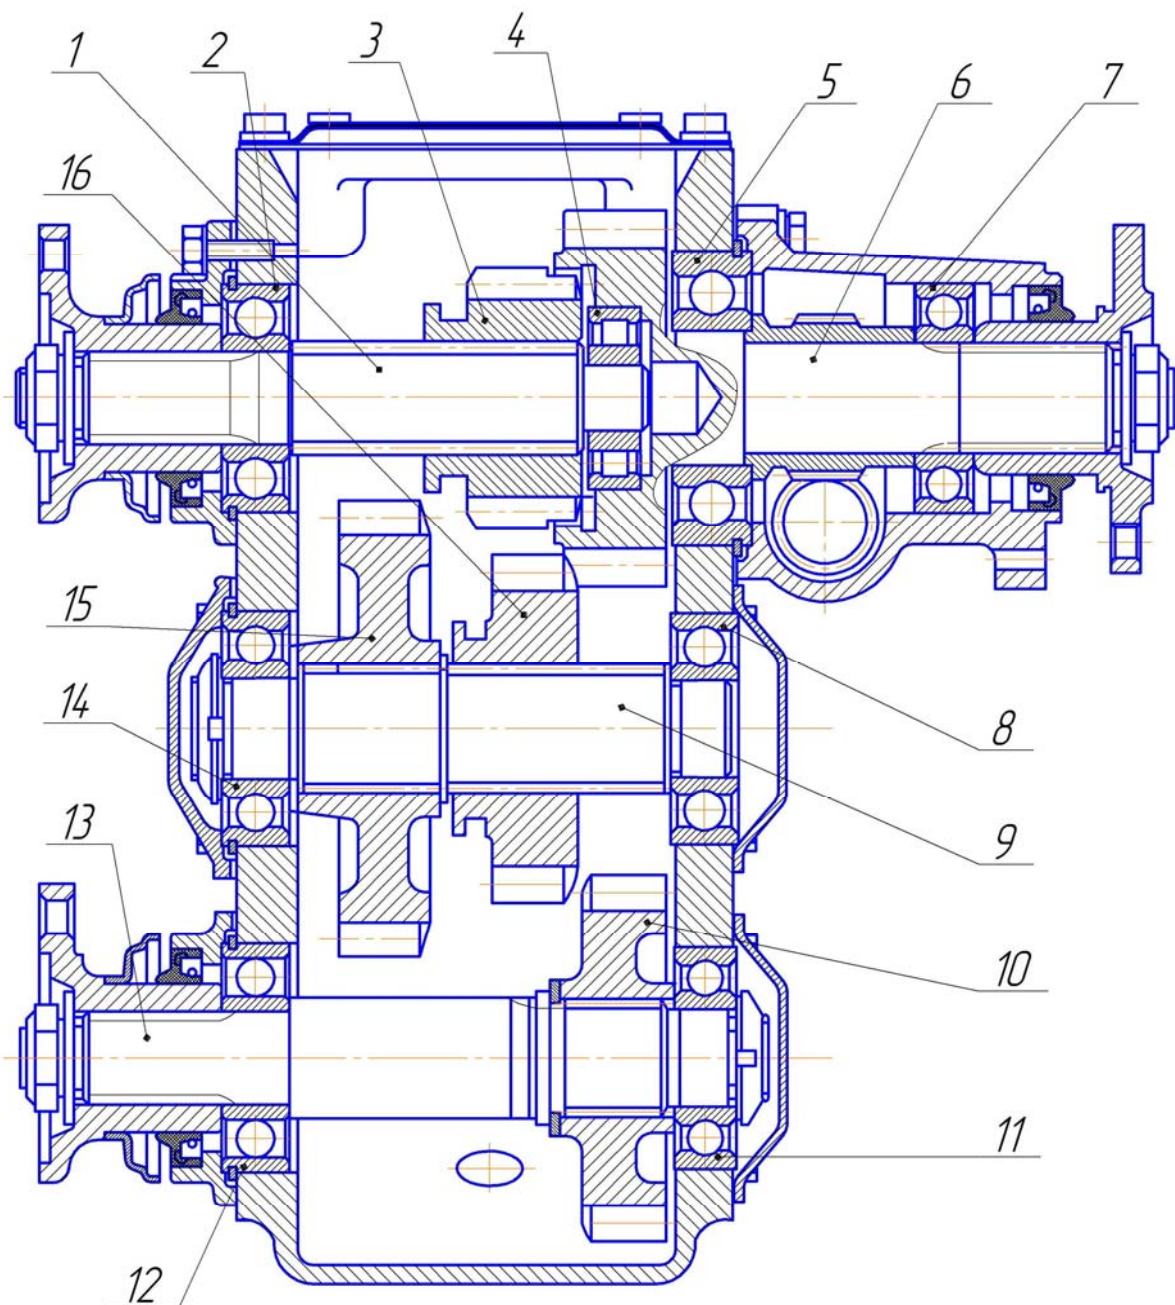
Раздаточная коробка автомобиля ГАЗ-66
